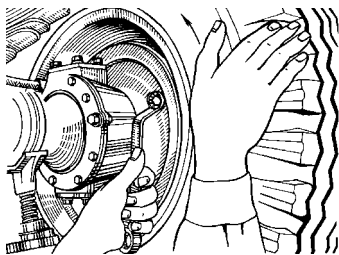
Регулировка зазоров между колодками и тормозным барабаном переднего колеса автомобилей УАЗ-31512, УАЗ-31514, УАЗ-31519
